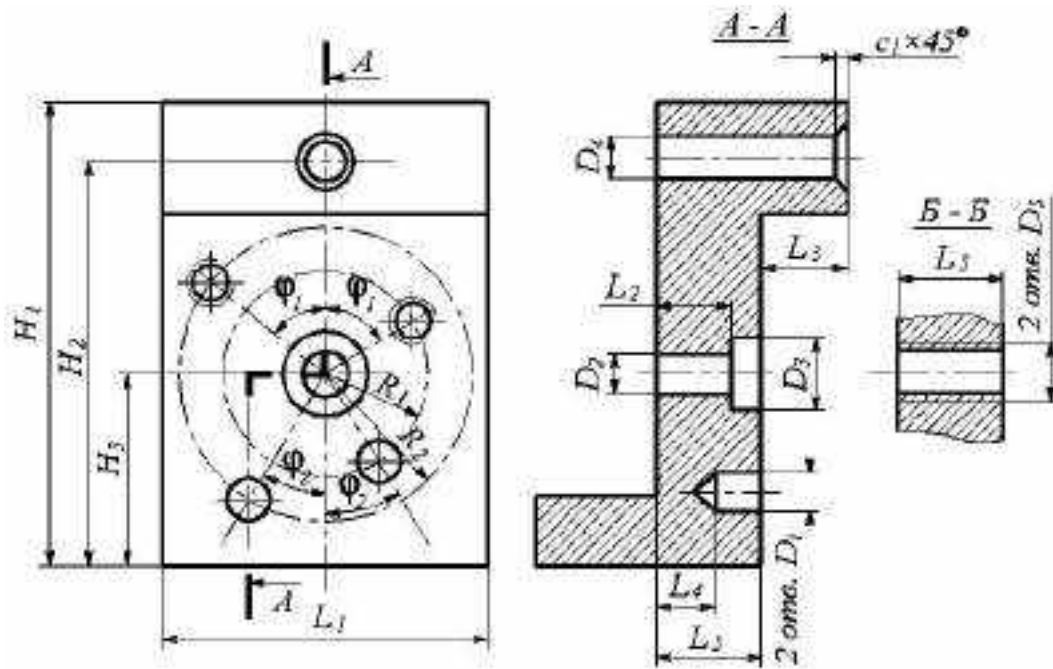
Эскиз обрабатываемой детали для вариантов 4, 9, 14, 19, 24
